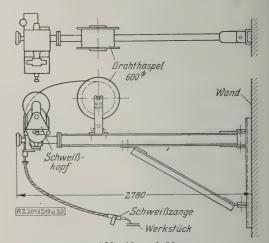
und 20 Halbselbsttätige Schweißeinrichtung zum Schweißen von Rohrnähten der General Electric Co., vertreten von der AEG, Berlin.
